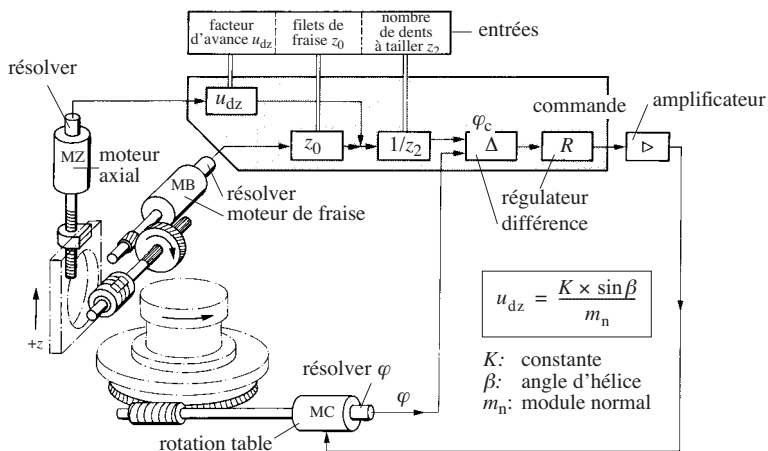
Schéma d'une machine à tailler les engrenages à commande électronique (H. Pfauter, Ludwigshafen).
